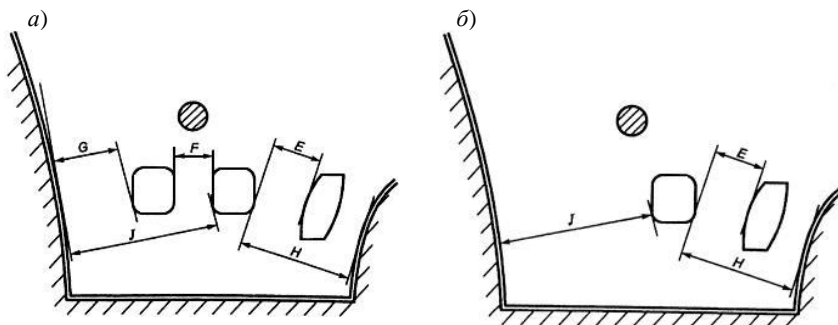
Размещение педалей управления легковым автомобилем: а – с механической коробкой передач; б – с автоматической коробкой передач
